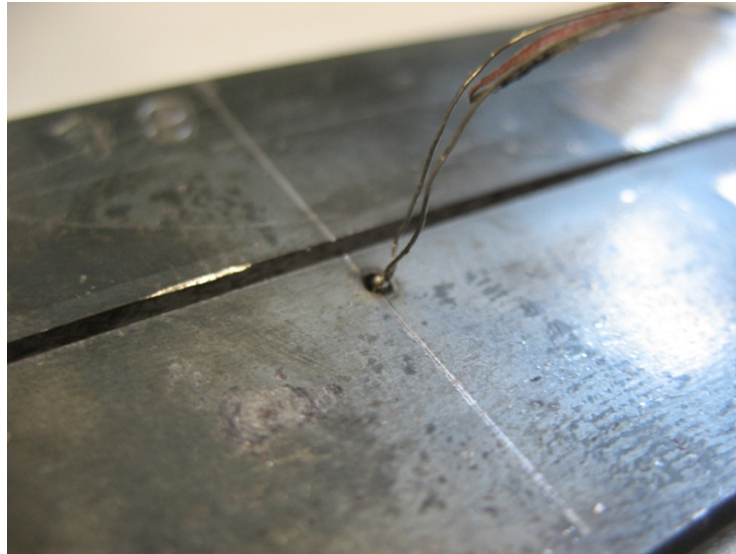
Ilustração da posição do termopar na placa de teste em relação à junta de soldagem
